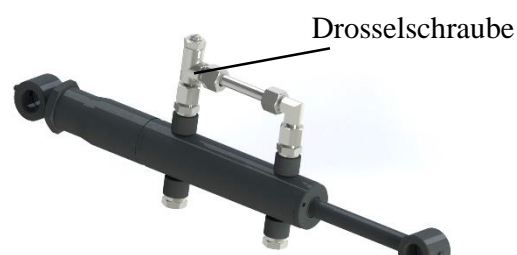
HYDRAULIKZYLINDER FÜR DÄMPFUNG
